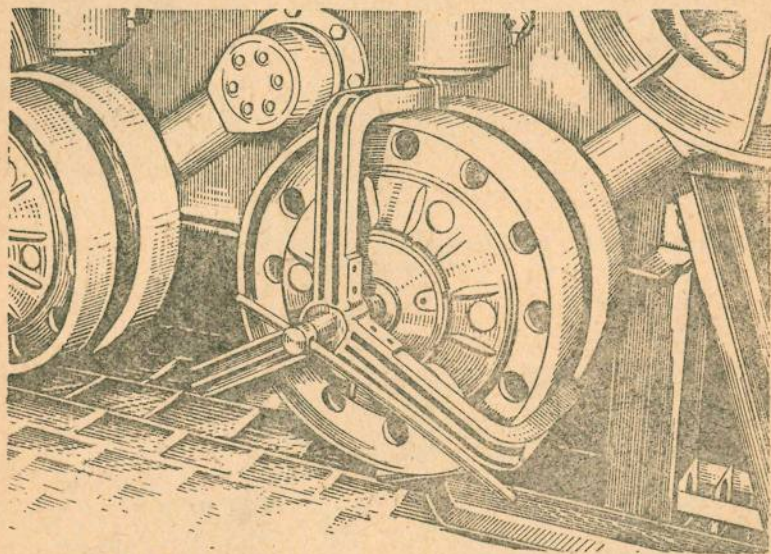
Обжатие крышки нижнего катка при помощи приспособления для установки пружинного кольца
